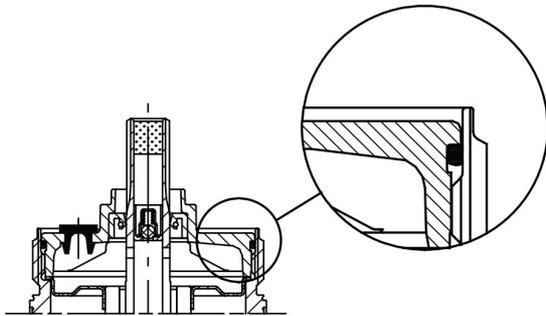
Крышка должна быть ниже верхнего торца двигателя
